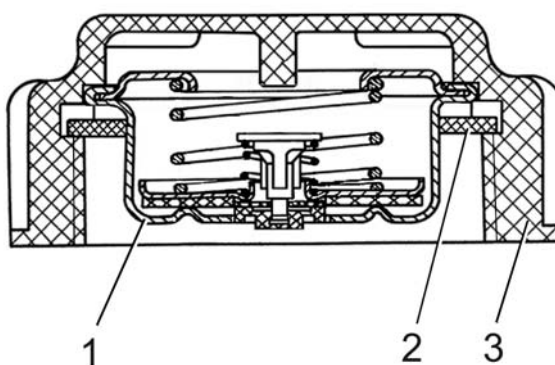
Пробка расширительного бачка: 1 - блок клапанов; 2 - прокладка; 3 - корпус
